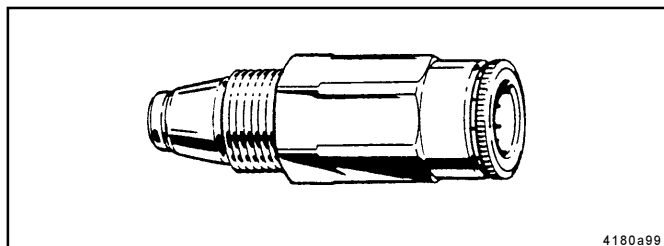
Rückschlagventil, steckbar mit gerändeltem Bund (Standard-Zange)
